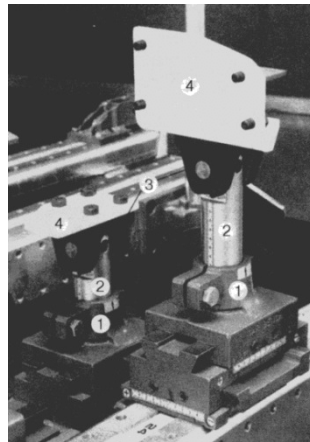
Многоэлементный угольник с универсальным адаптером для контроля автомобильных кузовов: 1 – перемещаемый по салазкам держатель для фиксации стойки угольника; 2 – стержень со шкалой для регулирования высоты; 3 – универсальный адаптер для крепления наконечника, который пригоден для любых автомобилей
